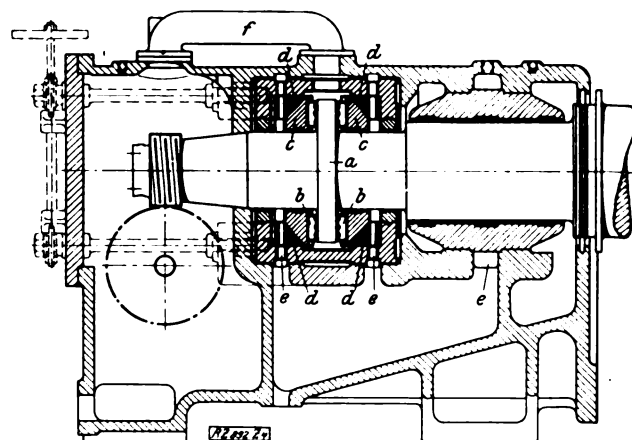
C. A. Parsons & Co., Ltd., Einstellbares Einscheiben-Drucklager der HD-Turbine.
